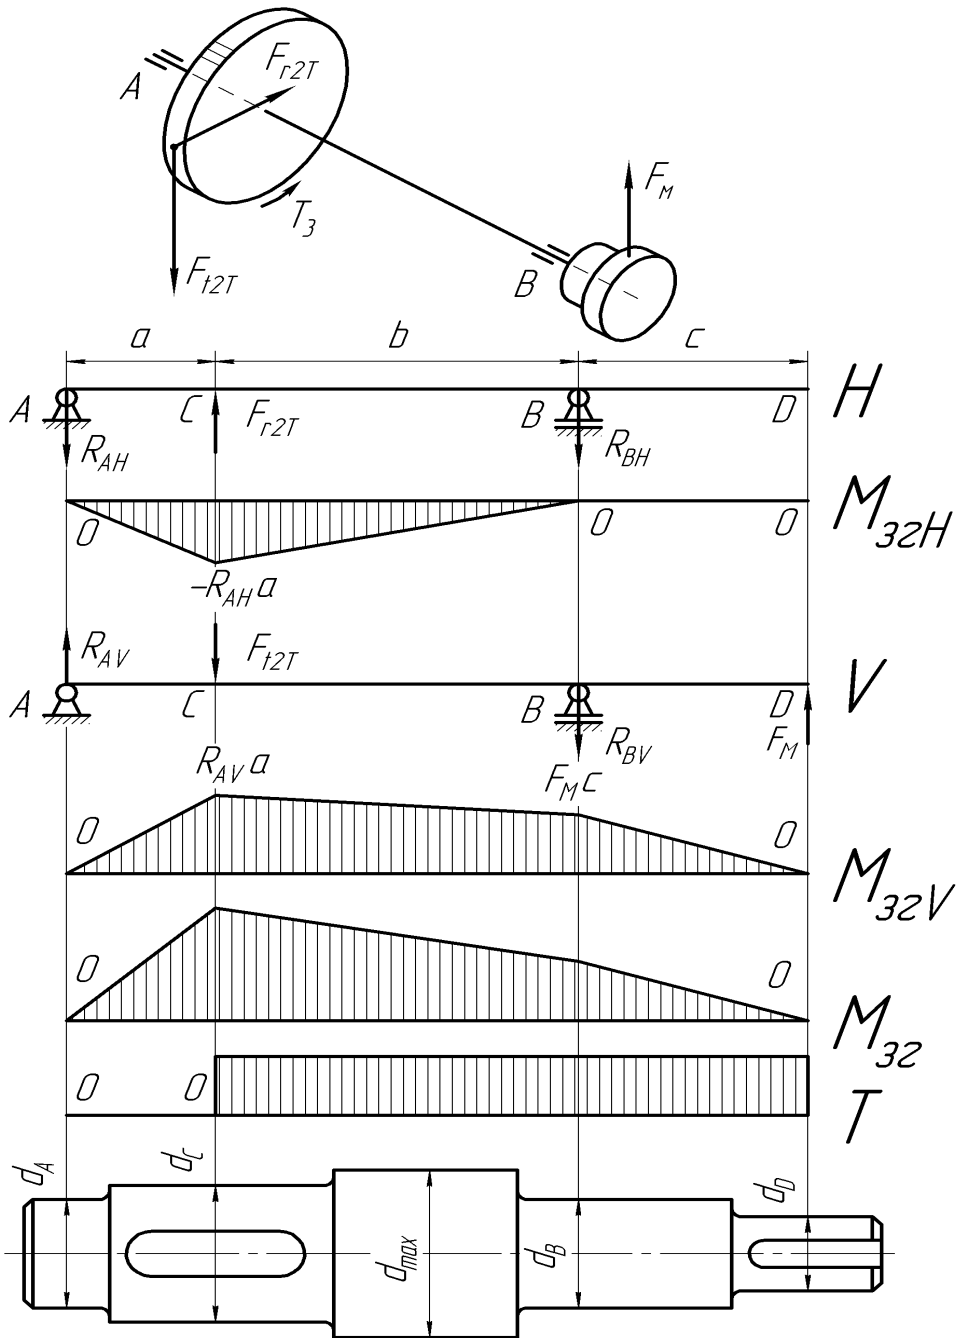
Розрахункова схема, епюри моментів і ескіз веденого вала циліндричного двохступінчастого редуктора
